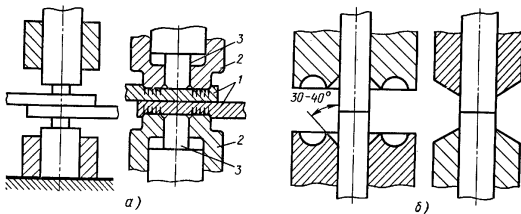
Схемы холодной сварки усилиями, нормальными к поверхности соединения:
